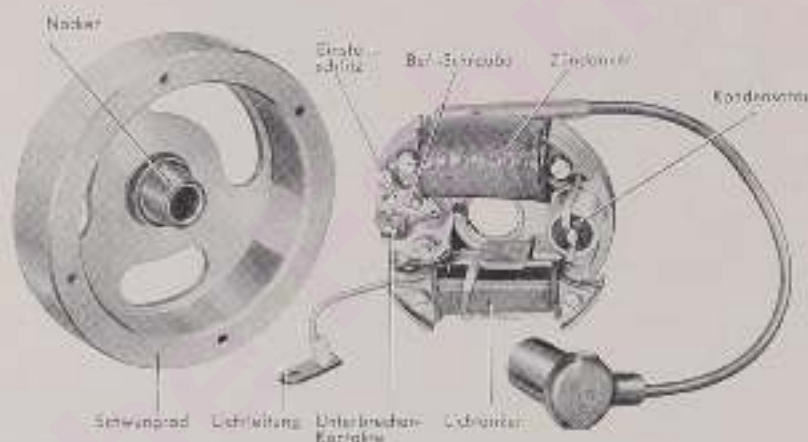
Bosch-Schwungradmagnetzylinder LM UP 1,115/17
